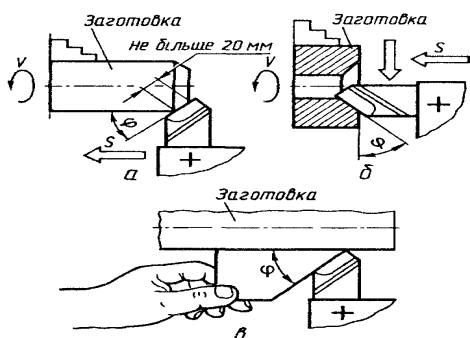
Обробка коротких конічних поверхонь широким різцем: а - зовнішньої поверхні; б - внутрішньої поверхні; в - установлення різця за шаблоном
